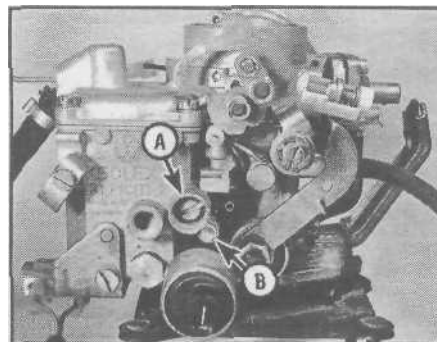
, 10. Расположение винтов регулировки оборотов холостого хода [А] и качества смеси [В]
